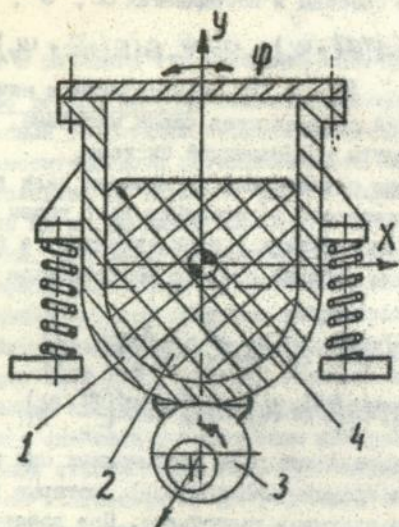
Схема установки для виброобработки деталей: 1-контейнер; 2-рабочая среда; 3-вибратор; 4-центр масс контейнера
